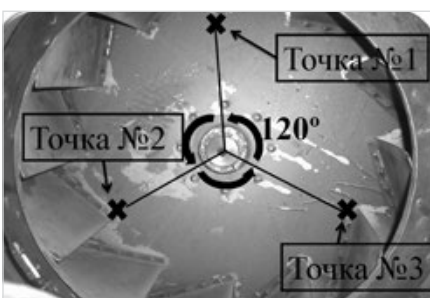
Точки установки пробного груза на рабочем колесе вентилятора
